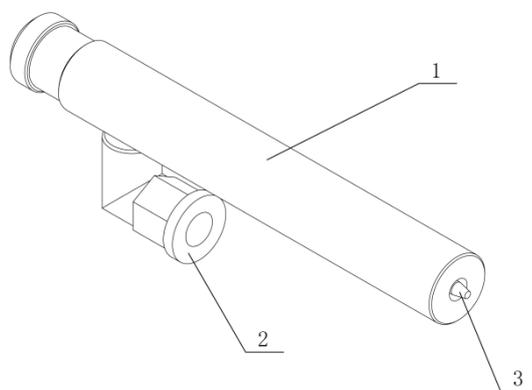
Верхний инструмент для втулок со сквозной резьбой и гаек
